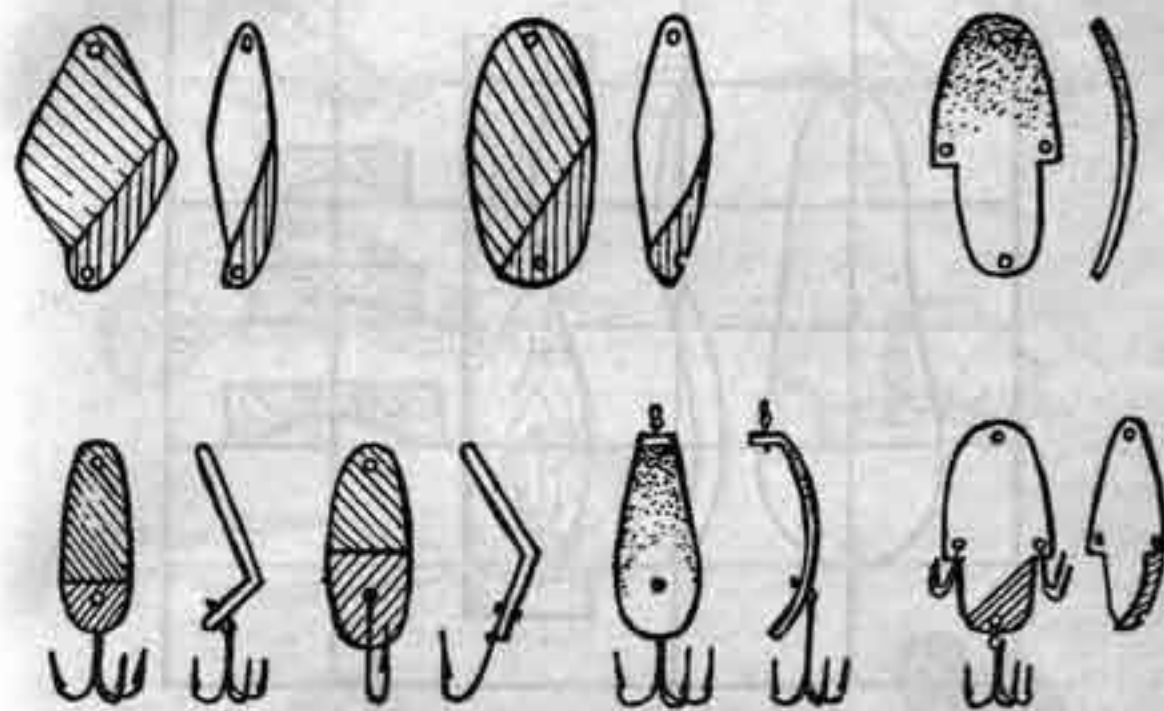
Заготовки и готовые плавноизогнутые и ломаные колеблющиеся блесны.
